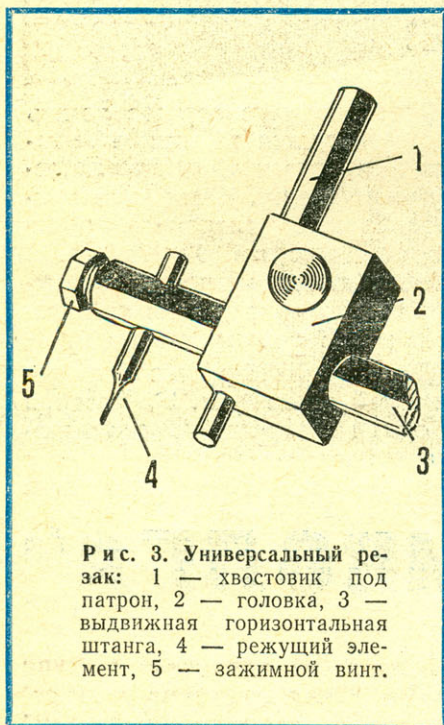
Универсальный резак: 1 — хвостовик под патрон, 2 — головка, 3 — выдвигаемая горизонтальная штанга, 4 — режущий элемент, 5 — зажимной винт.
